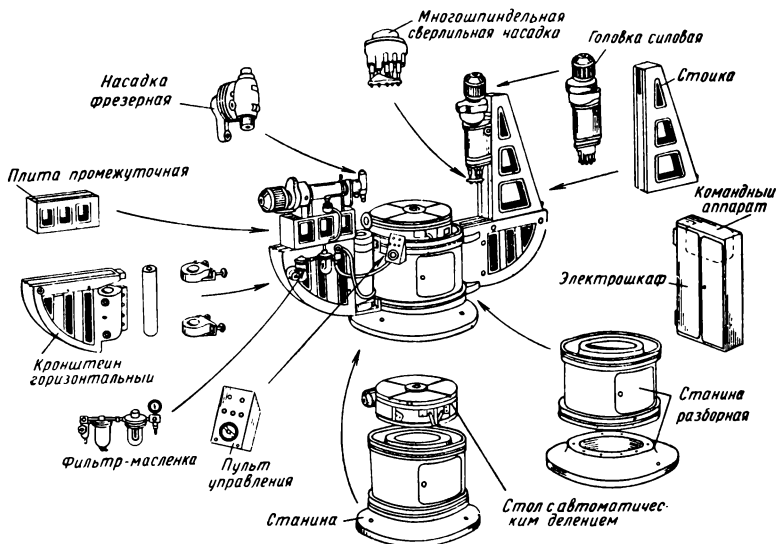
Агрегатный фрезерно-сверлильный станок с круглым столом
